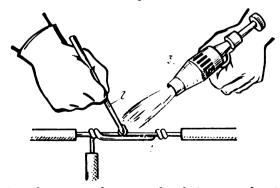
Lot d'outils et de dispositifs pour le soudage des brins des conducteurs et des câbles
